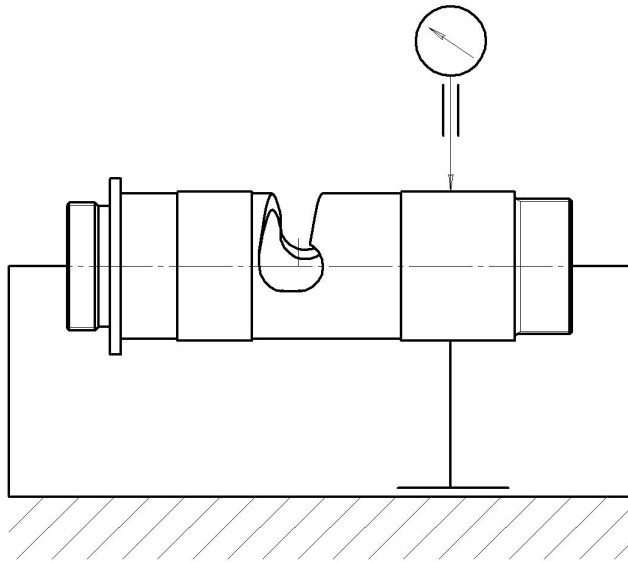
Схема вимірювання радіального биття циліндричної поверхні індикатором годинникового типу
